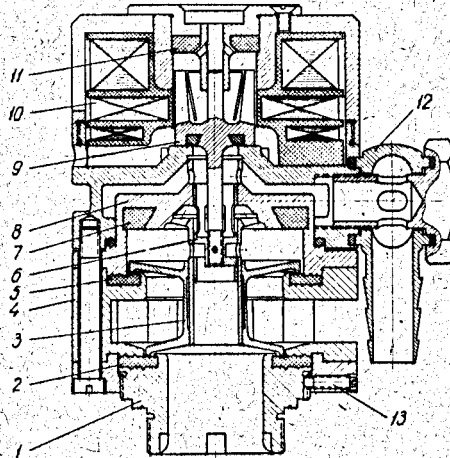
Двухступенчатый электромагнитный клапан двойного действия. 1 - юстировочное резьбовое кольцо; 2 и 5 - резиновые уплотнительные кольца; 3 - подвижная втулка с двумя уплотнительными грибками; 4 - корпус; 6 - золотник; 7 и 11 - резиновые амортизаторы; 8 - направляющая; 9 - плунжер; 10 - катушка электромагнита; 12 - цуцер; 13 - стопорный винт.
